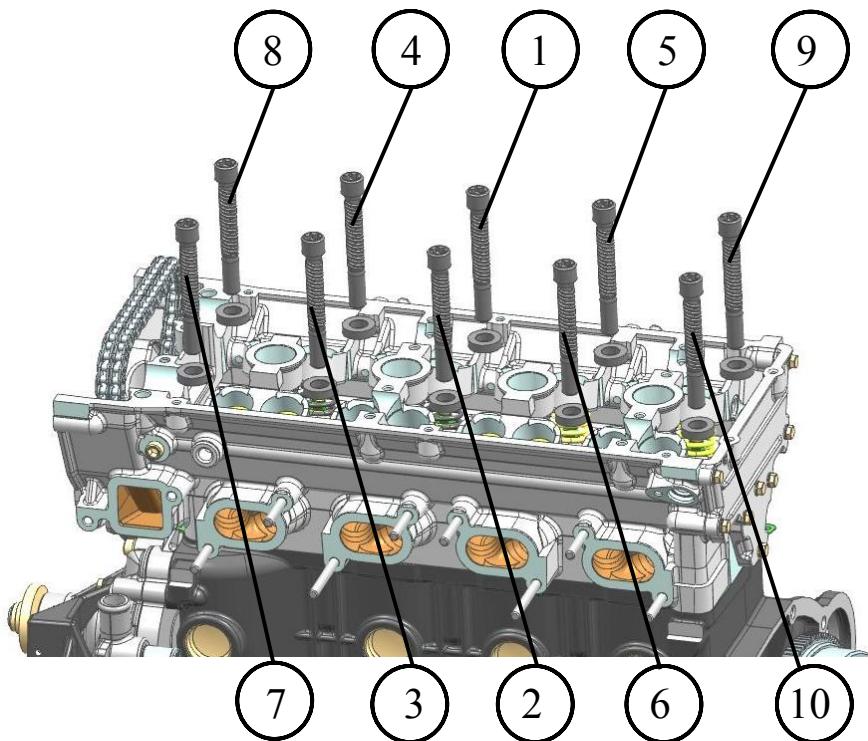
Последовательность затяжки болтов головки цилиндров двигателей с жёсткой (стальной) прокладкой головки цилиндров
